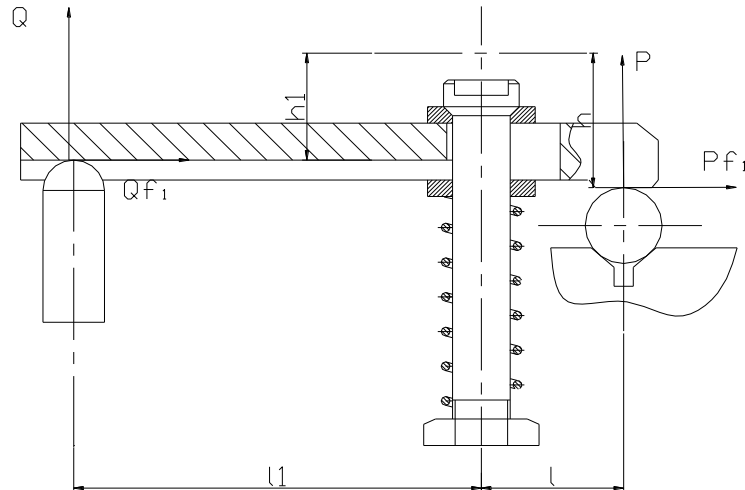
б – Схема для розрахунку зусилля закріплення деталі у пристрої.
